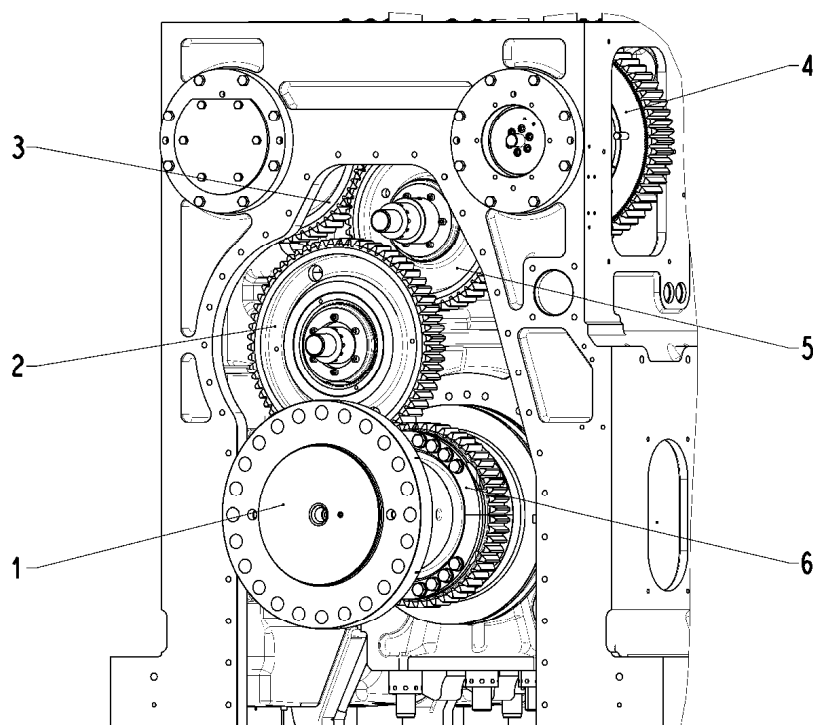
привод розподільчого валу двигуна: 1 – опорні підшипники розподільчого валу; 1 – фланець; 2, 5 – проміжна шестерня; 3 – шестерня приводу розподільчого валу; 4 – шестерня приводу валу ПНВТ
